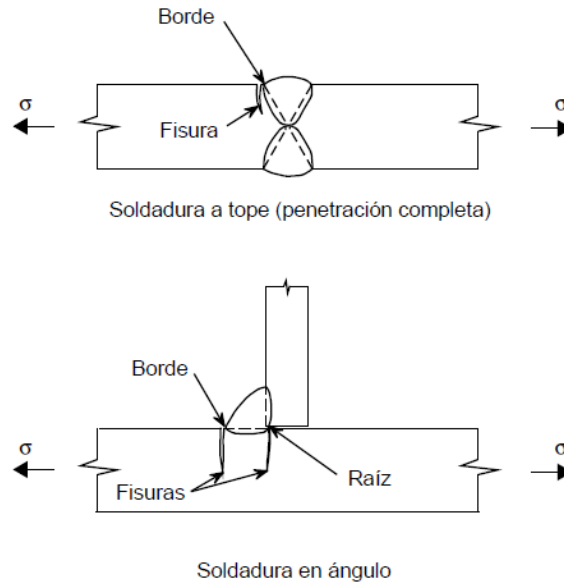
Concentración de tensiones por soldadura [19]
